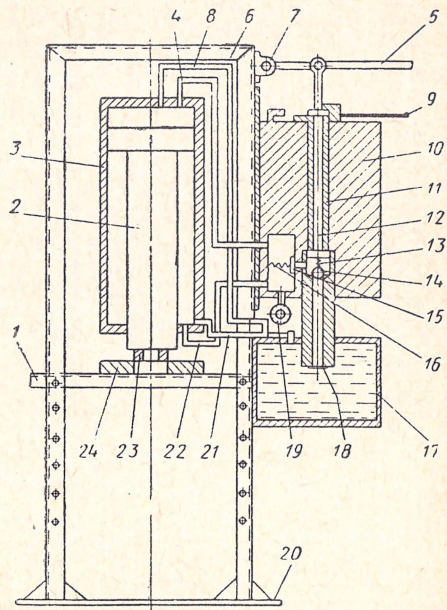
Пресс для облегчения прессования подшипников и втулок
